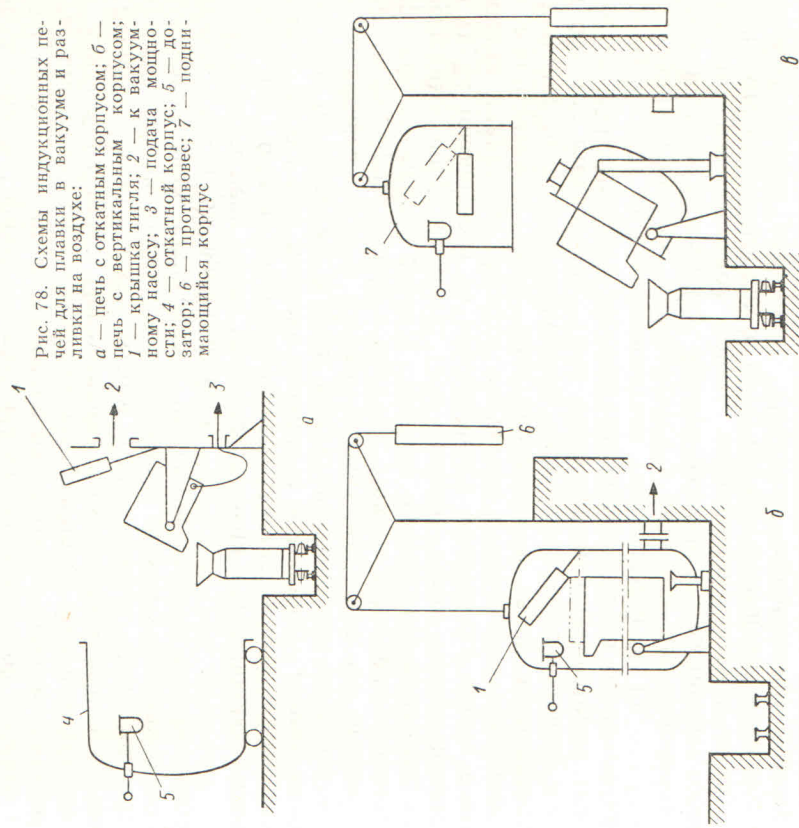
Схемы индукционных печей для плавки в вакууме и разливки на воздухе: а — печь с откатывающимся корпусом; б — печь с вертикальным корпусом; 1 — крышка тигля; 2 — к вакуумному насосу; 3 — подача мощности; 4 — откатной корпус; 5 — двигатель; 6 — противовес; 7 — поднимаящийся корпус
